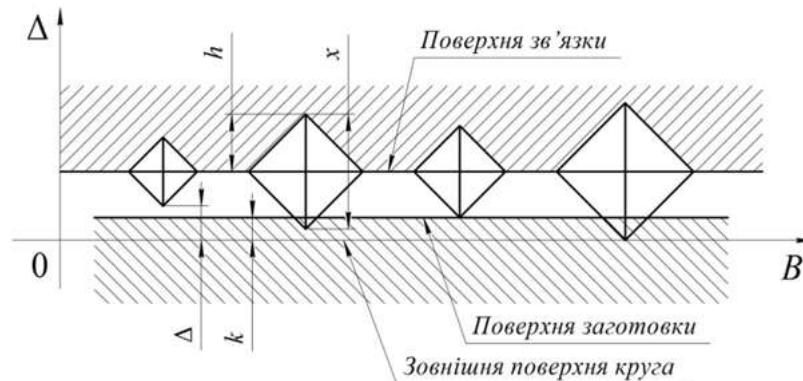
Взаємодія поверхні круга з поверхнею заготовки
